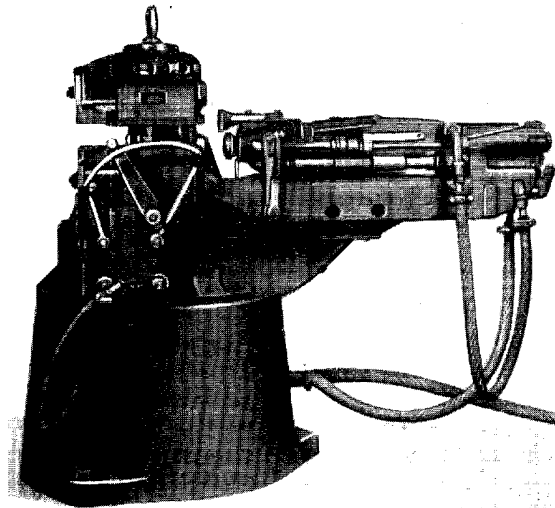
Bedienungsseite der Bohrkopf-Schmiedemaschine, Maschinenkopf gehoben
